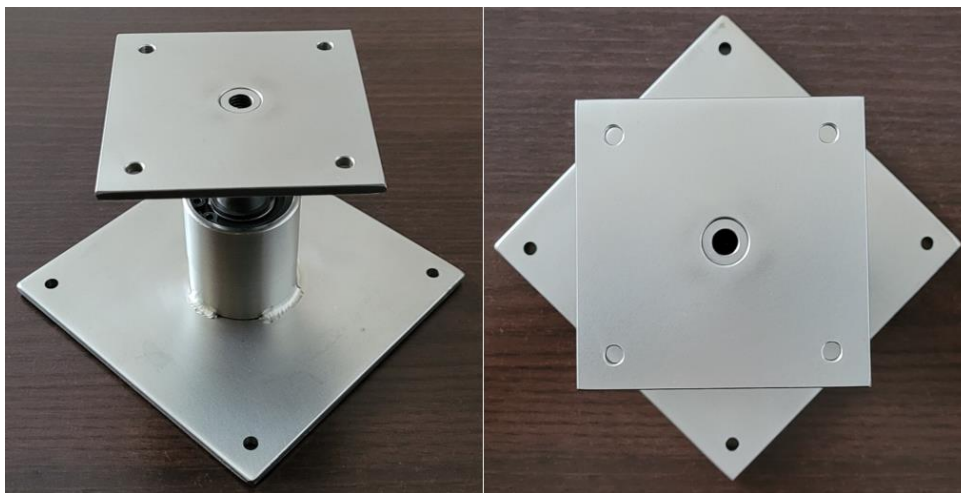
Držák horního DC motoru (pro pohyb v elevaci)
